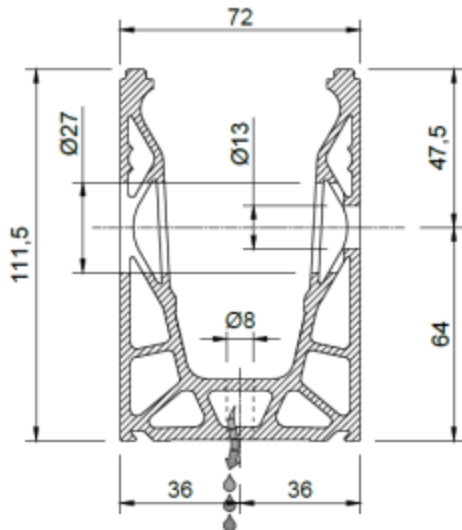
section transversale du profilé DF88FR.60 avec indication de perçage pour drainage
